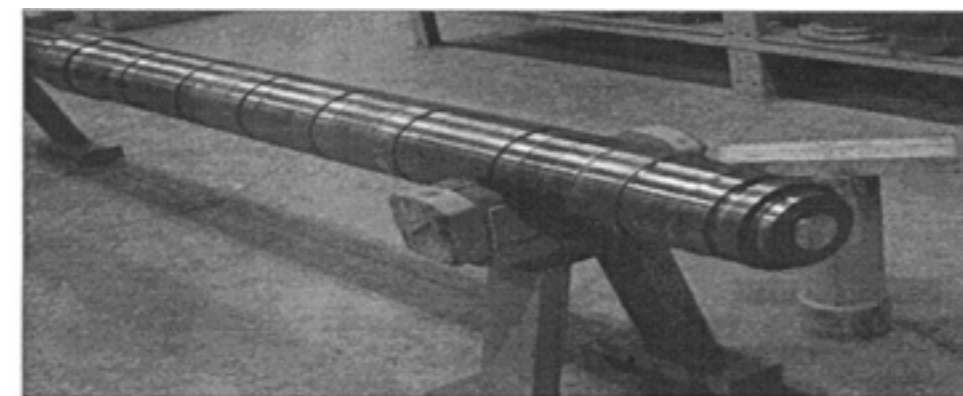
Корпус уплотнения и вал с усталостной трещиной. Вид 3
